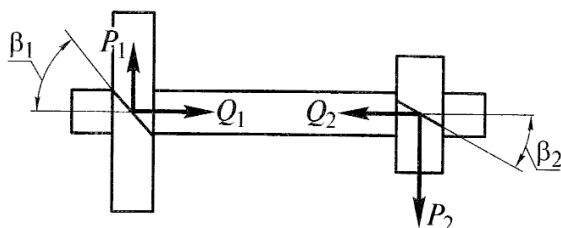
Схема сил, действующих на косозубые шестерни промежуточного вала
